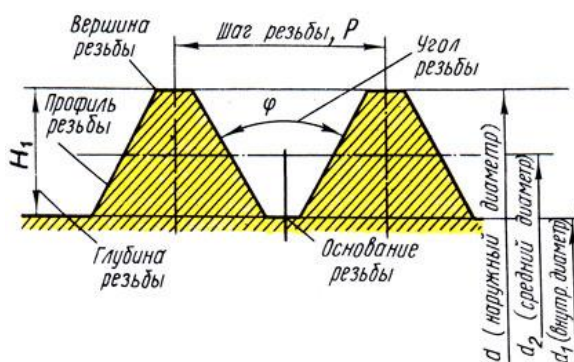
Элементы резьбы шага даётся число ниток (витков) на длине одного дюйма
